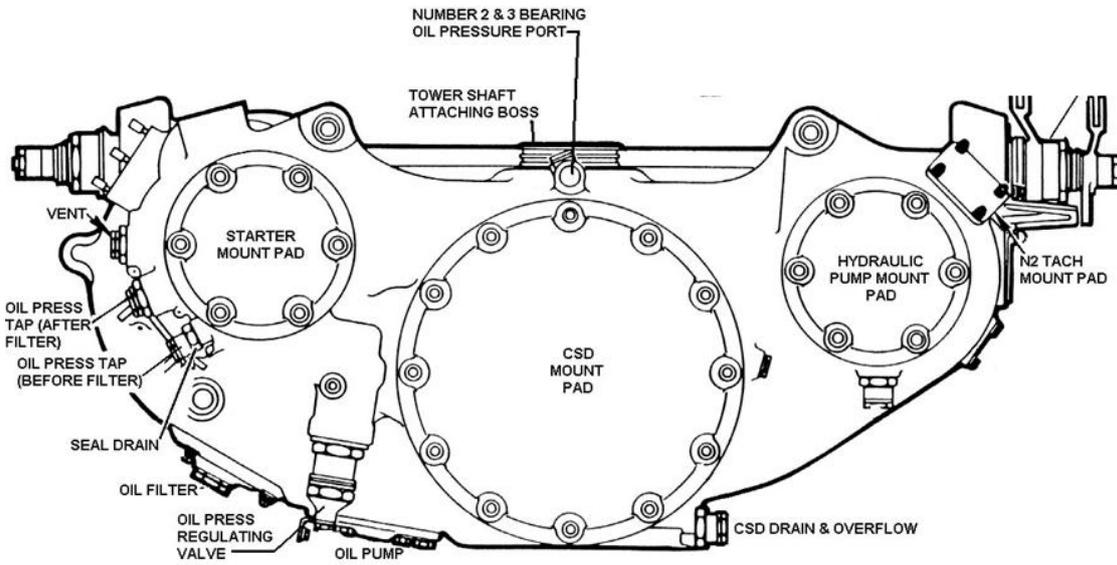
Lubricación de los cojinetes y de la caja de engranajes
